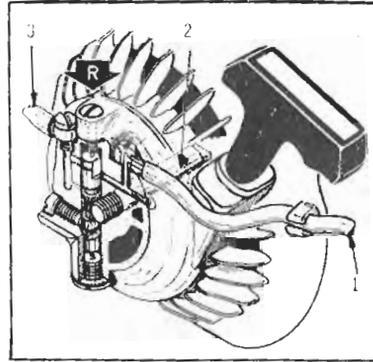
Bomba automática de rotor montada sobre el sistema de arranque.
